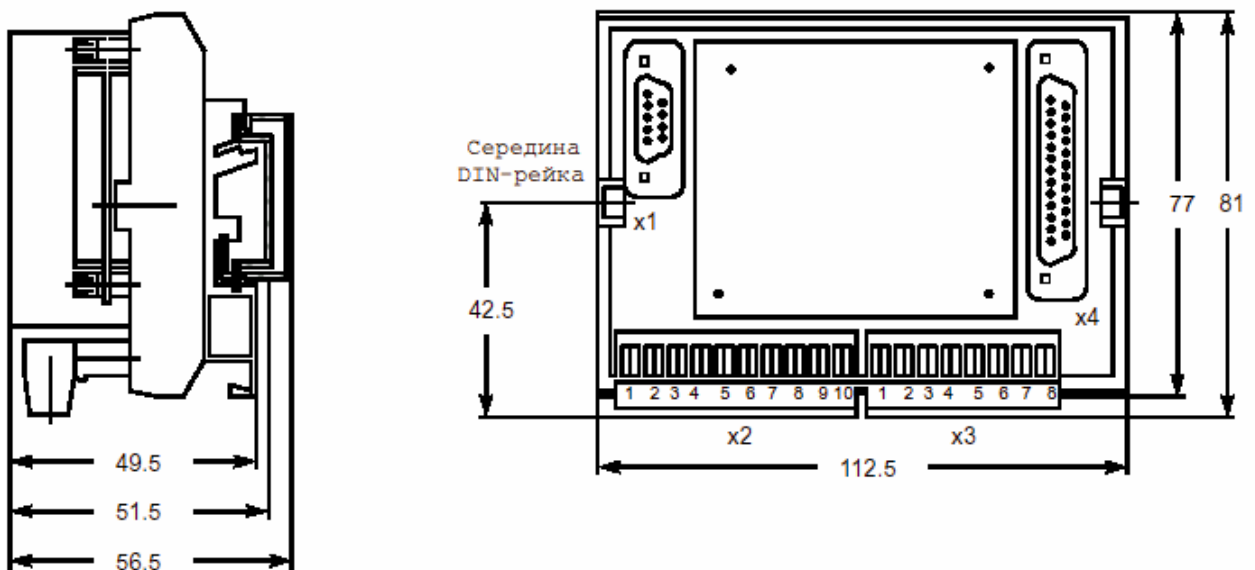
Габаритный чертеж SIPART шинное задающее устройство, размеры в мм
